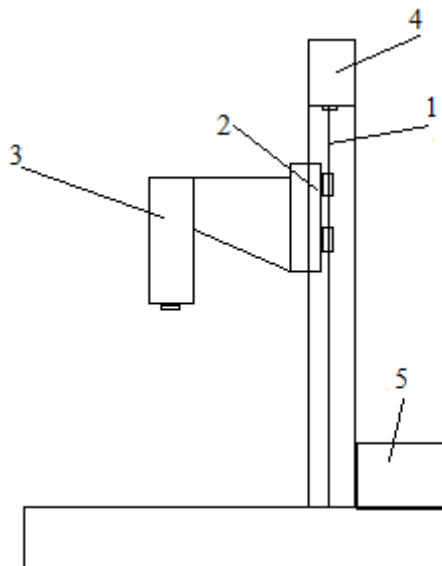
Цифровой вертикальный дальномер: 1 – ходовой винт, 2 – салазки, 3 – измерительная головка, 4 – шаговый двигатель, 5 – цифровое устройство
